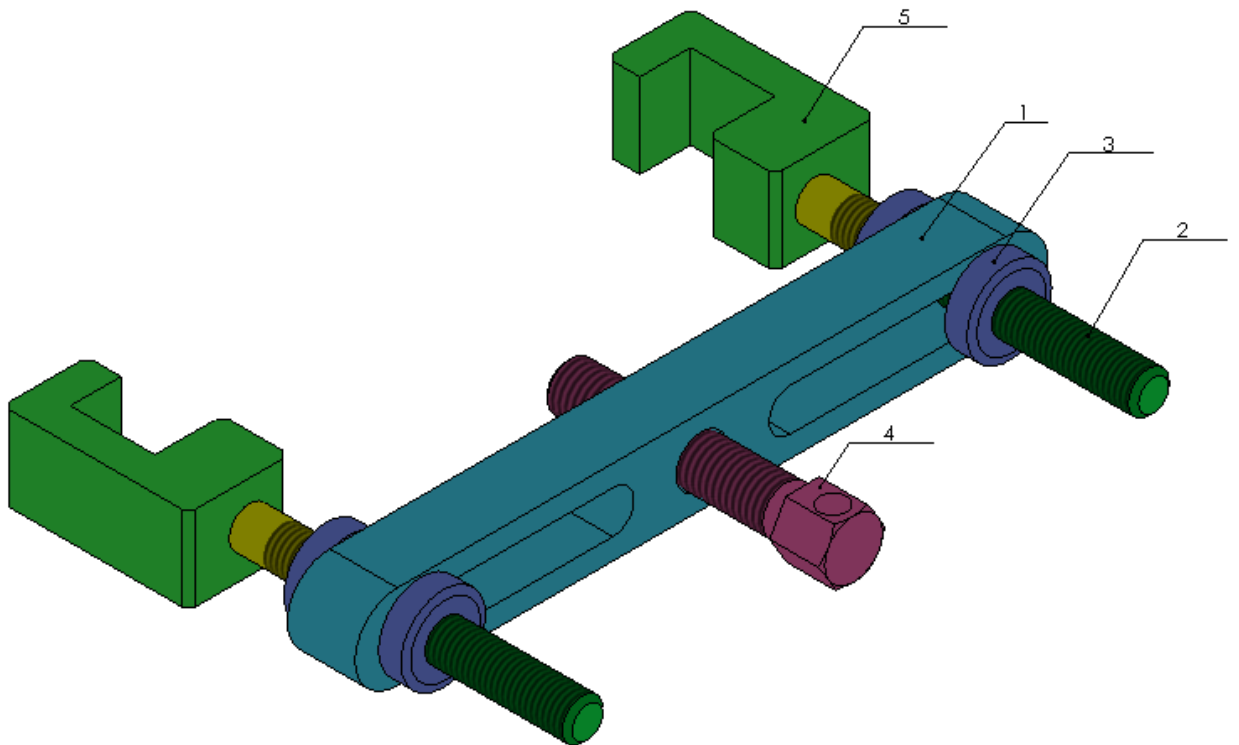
Универсального устройства съемника шкива коленчатого вала: 1 – планка, 2 – шпилька (4 шт.), 3 – гайка (4 шт.), 4 – винт, 5 - зацеп
